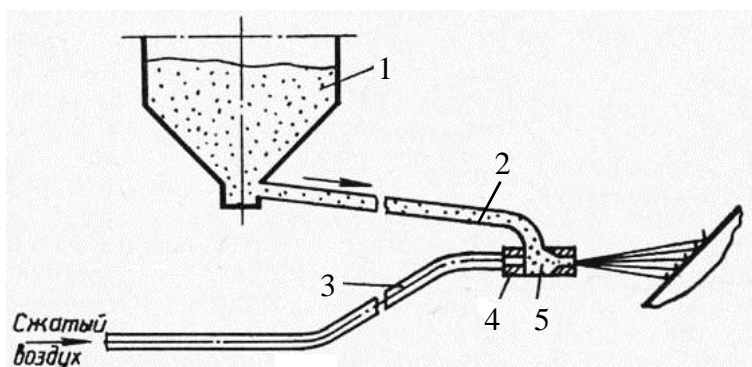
Схема абразивоструйного аппарата всасывающего действия: 1– бункер; 2 – рукав для подачи абразива в сопло; 3 – воздушный рукав; 4 – пескоструйный пистолет; 5 – смешивательная камера.
